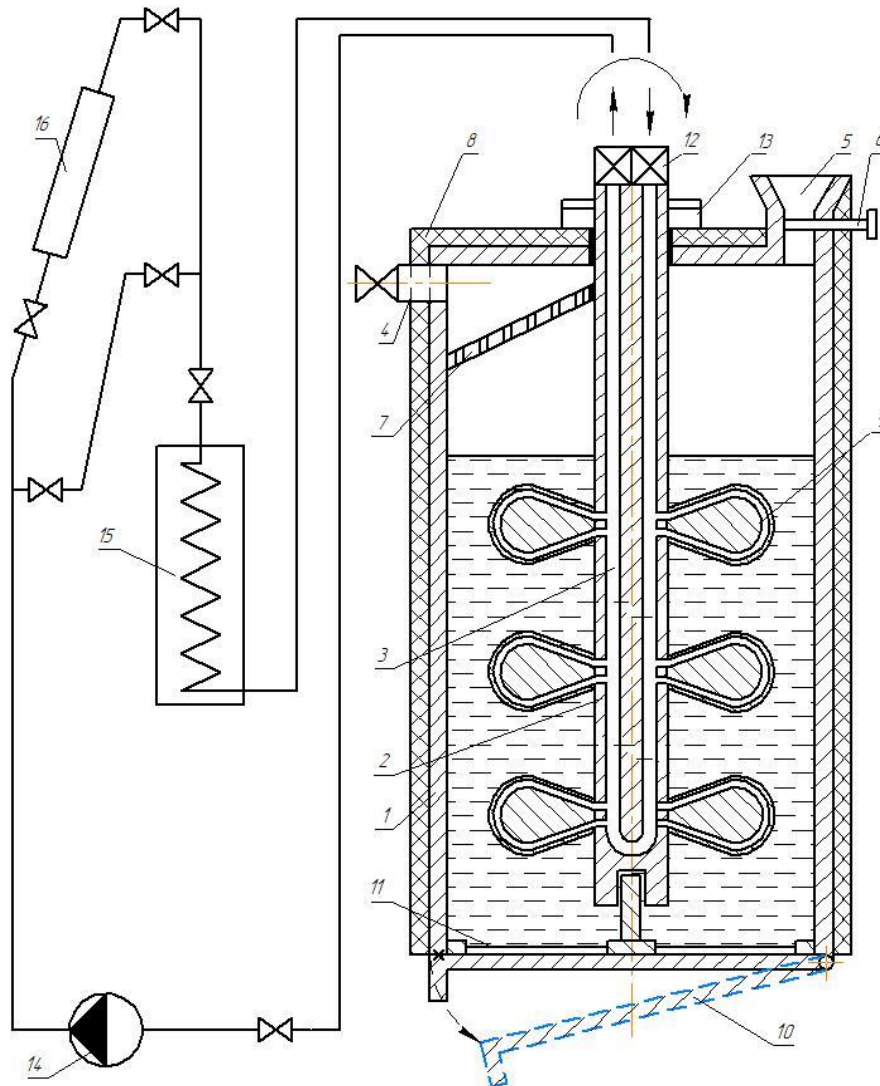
Конструктивна схема біогазової установки із сонячним колектором
